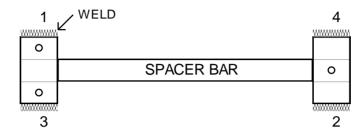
Secuencia de Soldado para los Bloques de Montaje
